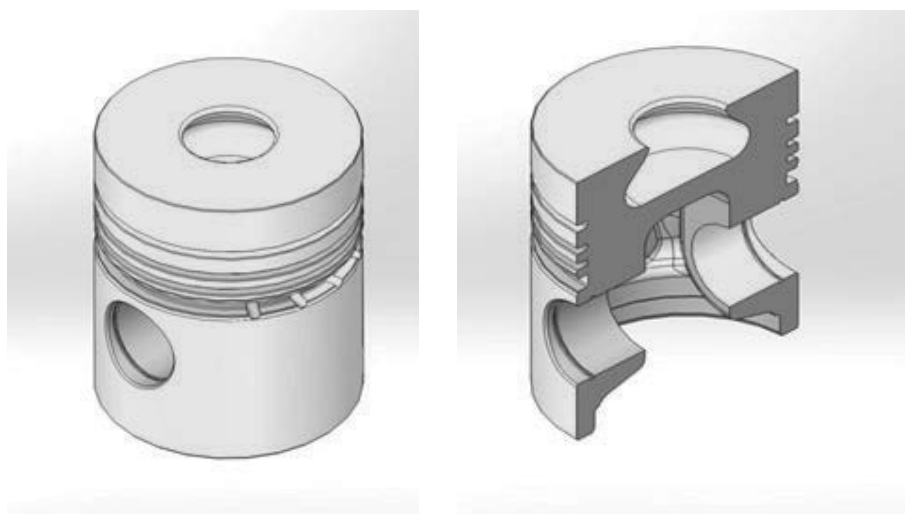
3D-модель литой детали поршня Д 240-1004021
